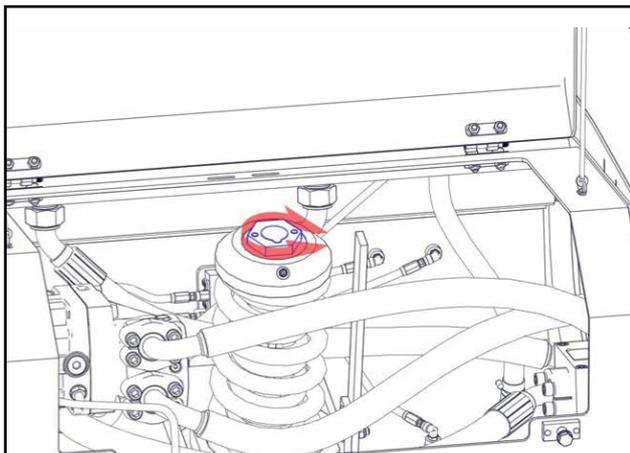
Пластина механизма рычажного типа – Затяжка пружины натяжения.
